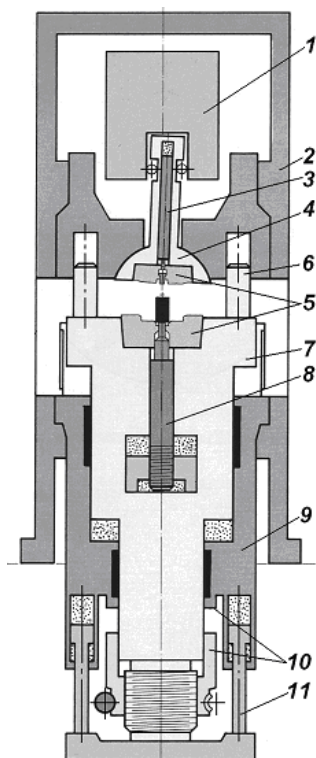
Конструктивная схема пресса для ШСО модели Т-630, (где: 1 – привод механизма обкатывания; 2 – станина; 3 – верхний приводной пуансон; 4 – активный прессователь; 5 – инструмент; 6 – направляющие; 7 – ползун; 8 – нижний выталкиватель; 9 – корпус гидроцилиндра; 10 – упор; 11 – возвратные цилиндры)
